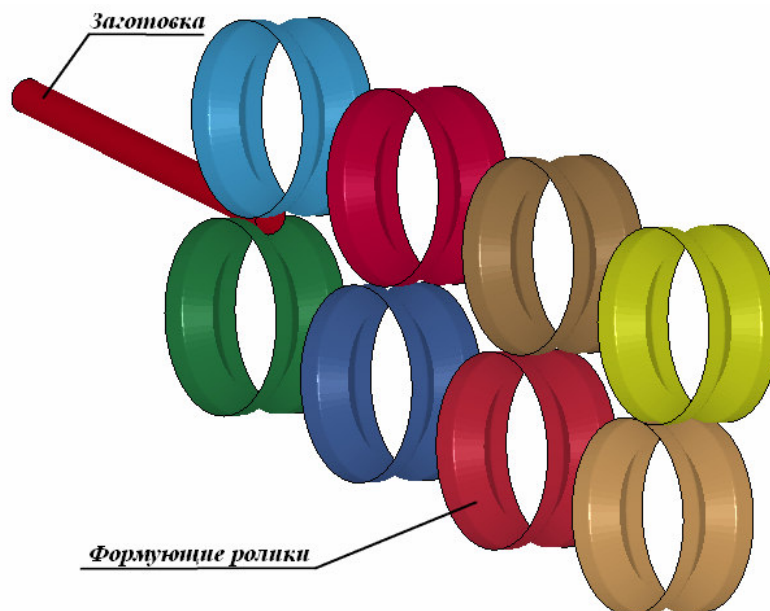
Формообразующая оснастка (4 пары роликовых калибров) для изготовления профиля 32x32x2,5мм
